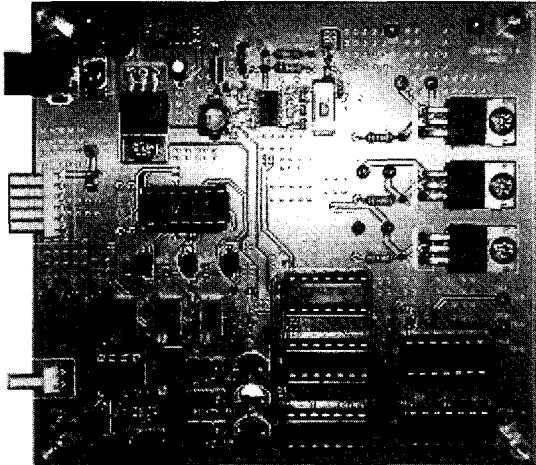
3파장 LED 백라이트 구동용 PCB 보드
